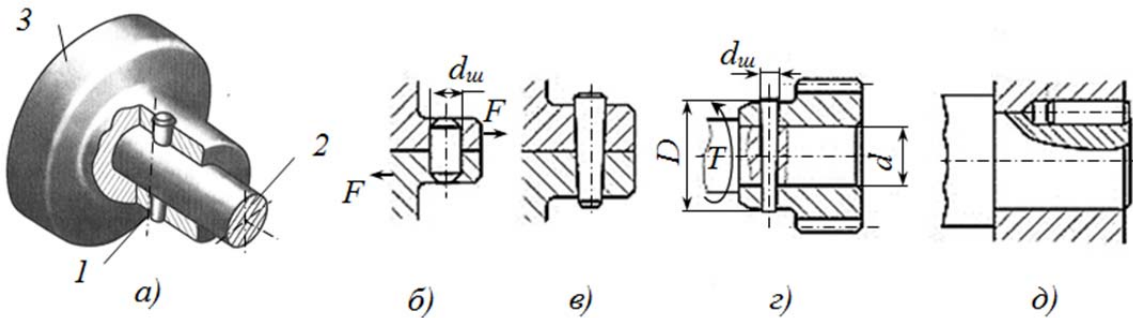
Штифтові з'єднання: загальний вигляд (а), схеми з'єднань штифтами (б-д); 1 – штифт; 2 – вал; 3 – маточина деталі.
